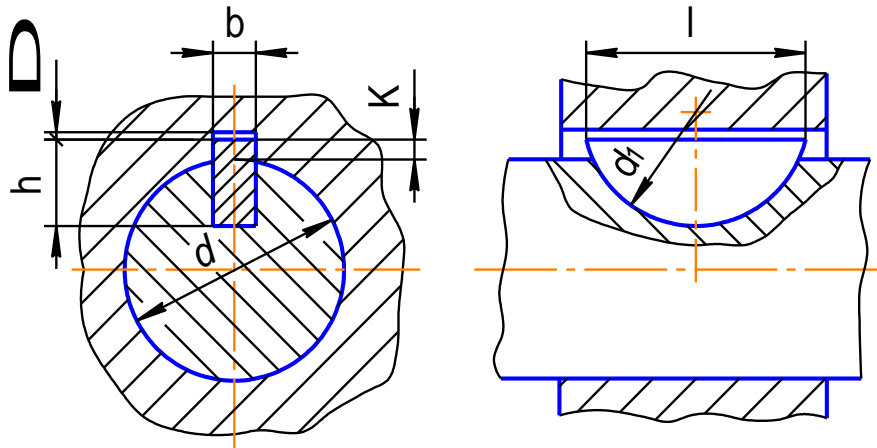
Конструкція шпонкового з'єднання з сегментною шпонкою
